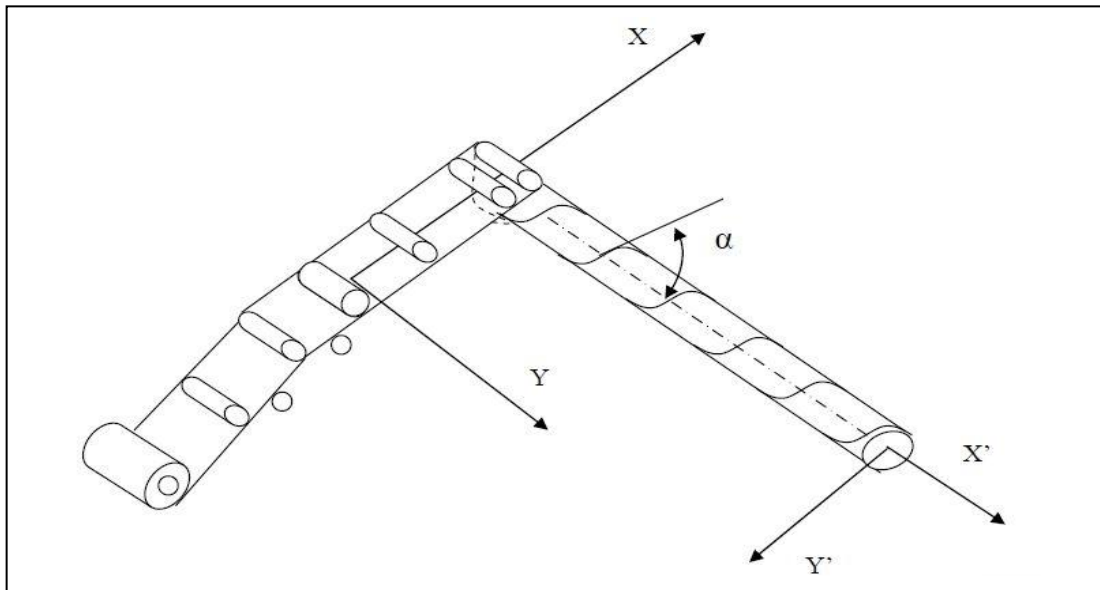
Technique de fabrication des tubes soudés en spirale
